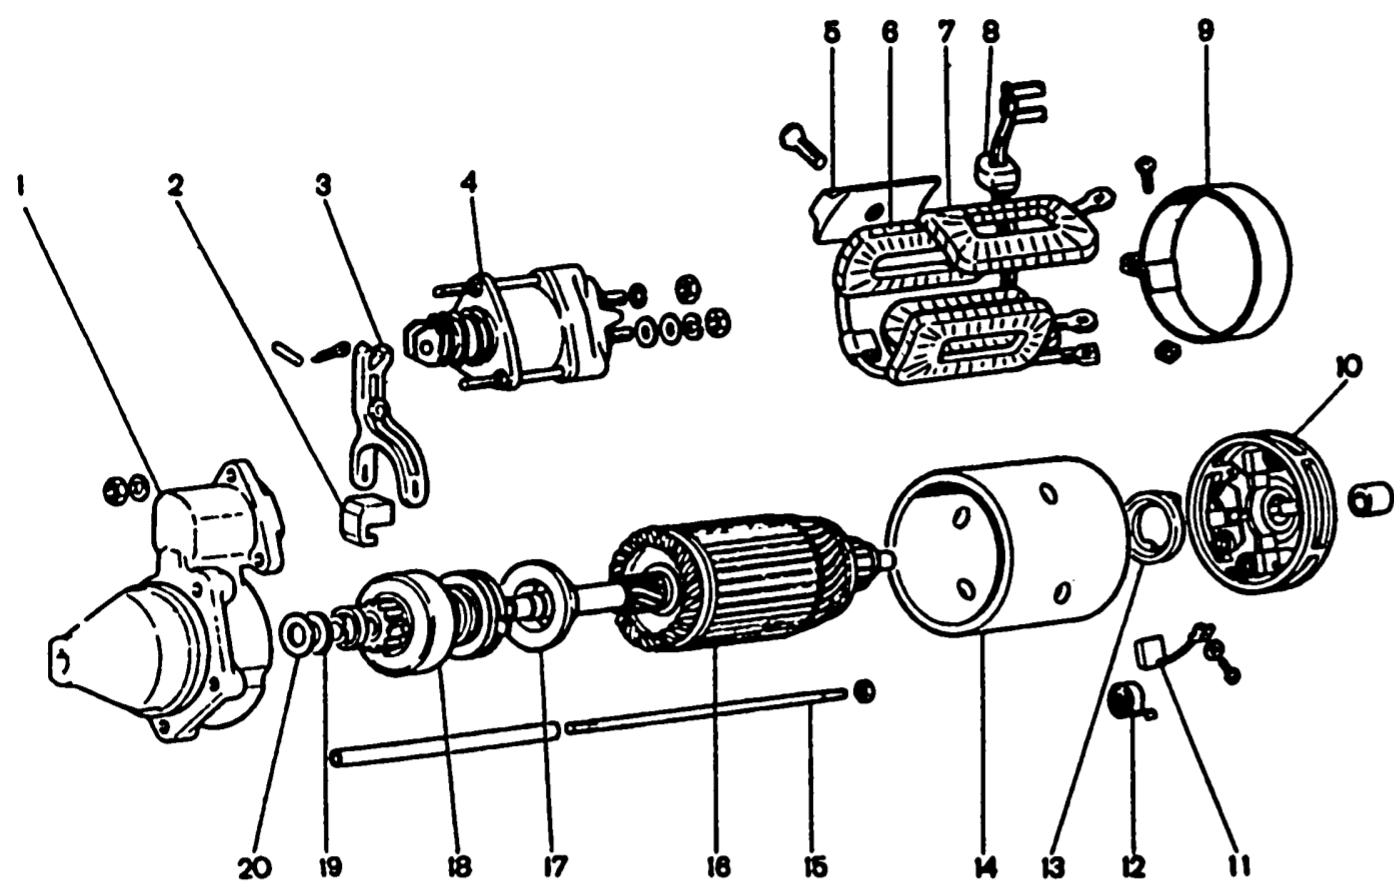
Детали стартера СТ-221: 1 - крышка стартера со стороны привода; 2 - резиновая заглушка; 3 - рычаг привода; 4 - тяговое реле; 5 - полюс статора; 6 - серийная обмотка статора; 7 - шунтовая обмотка статора; 8 - резиновая заглушка; 9 - защитная лента; 10 - крышка со стороны коллектора; 11 - щетка; 12 - пружина щетки; 13 - тормозной диск крышки; 14 - корпус; 15 - стяжная шпилька; 16 - якорь; 17 - ограничитель хода шестерни; 18 - обгонная муфта с шестерней привода; 19 - упорная шайба; 20 - регулировочная шайба
